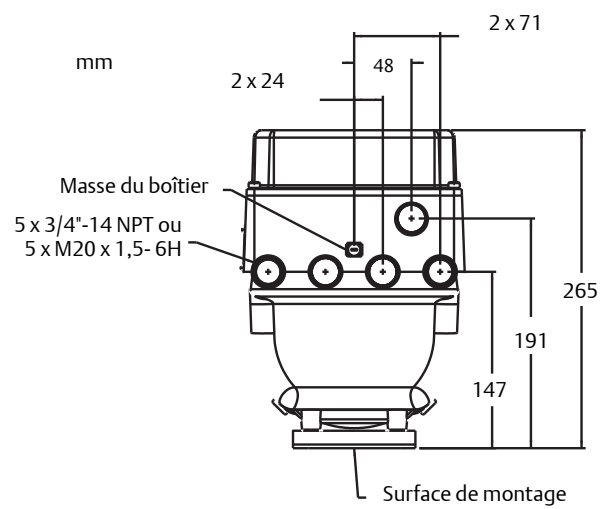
Dimensions, vue de dessusFigure 1-4 : Dimensions, vue des entrées de câble
